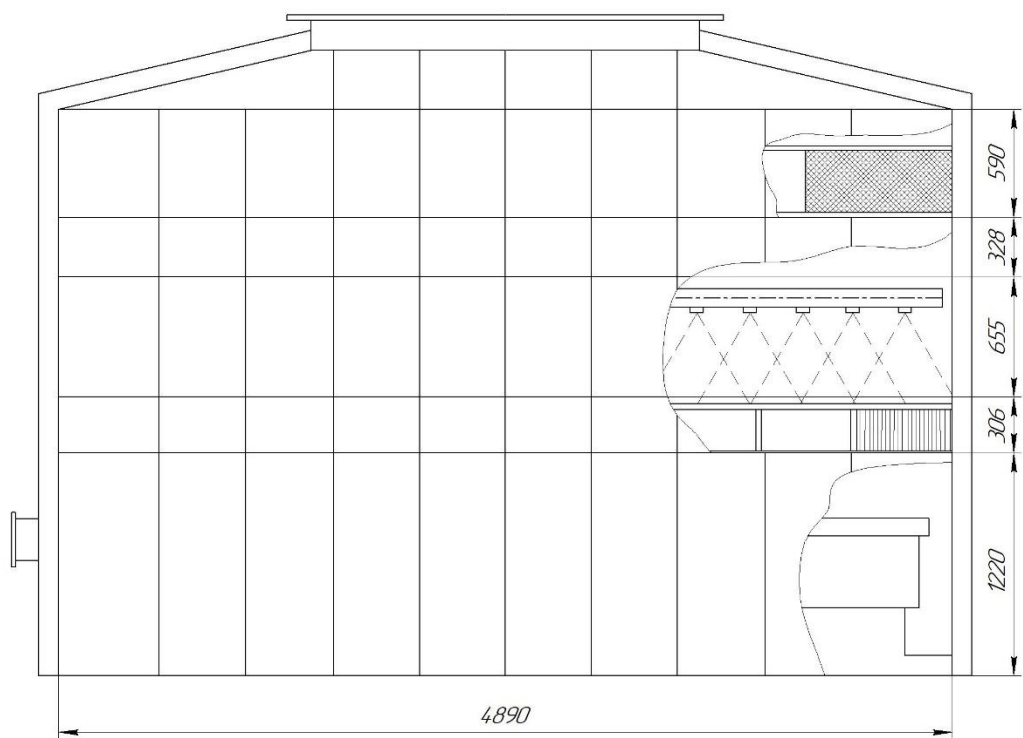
Габаритно-компоновочний ескіз контактного газопарового конденсатора
